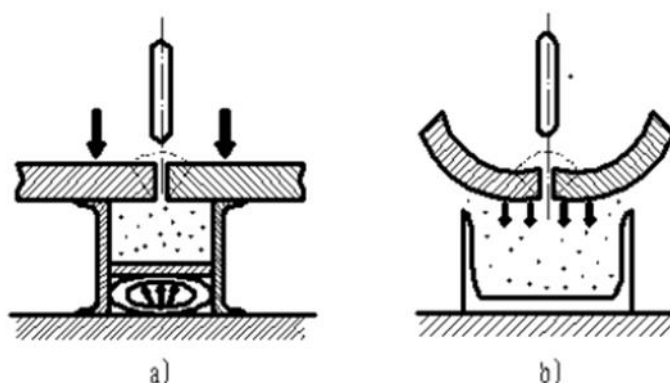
Принципиальная схема сварки с флюсовой подложкой
